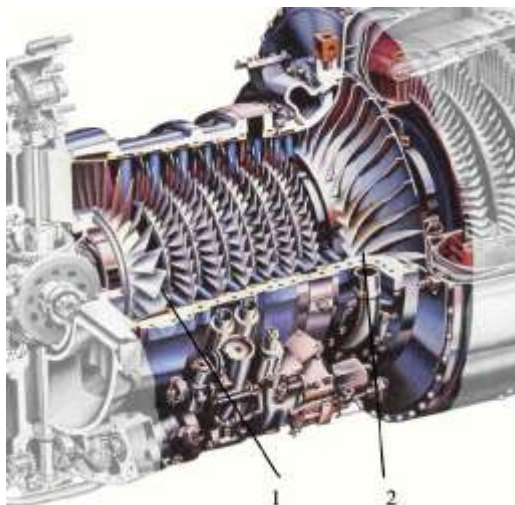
Внешний вид агрегата наддува двигателя внутреннего сгорания.
